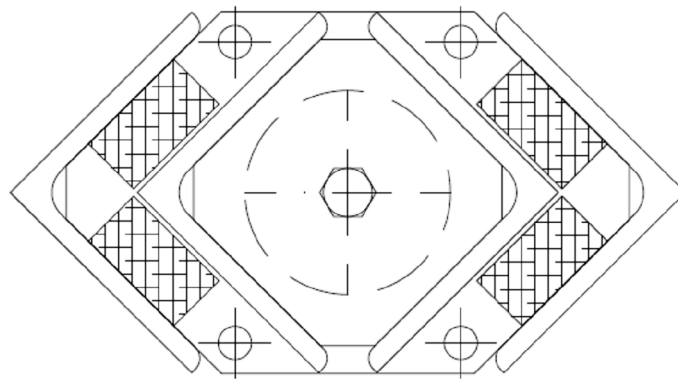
ó Plano amortiguador proyecto real 4. Vista en planta
